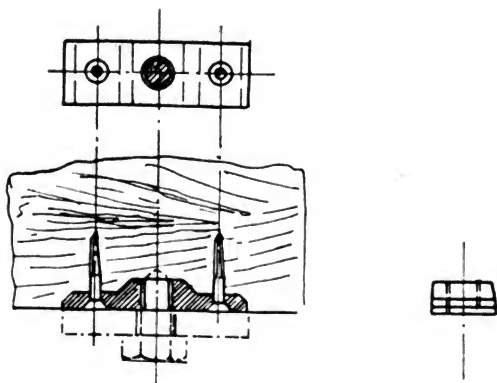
Anschraubplatten zur Karosseriebefestigung.
